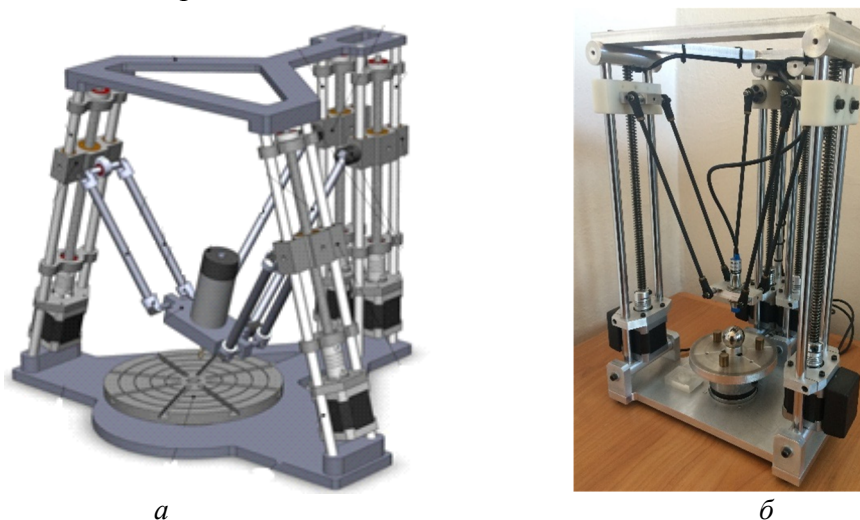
3D-модель пятикоординатного фрезерного станка каркасной компоновки (а) и внешний вид координатно-измерительной машины (б) на его базе
